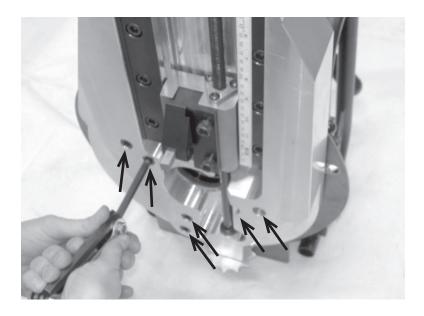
Затяните невыпадающие винты в 6 шт. отверстиях для крепления однорезцового суппорта на основном валу.
